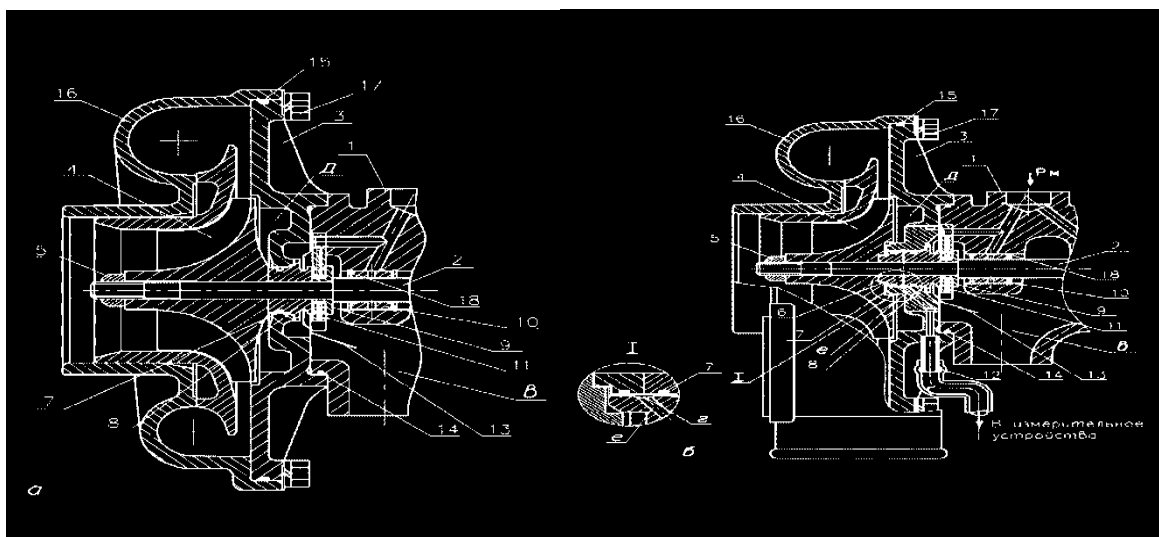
Компрессорная ступень турбокомпрессоров ТКР 7С:
